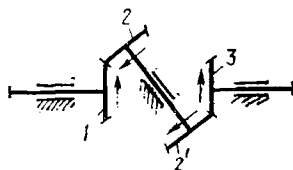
Двухступенчатый зубчатый механизм с коническими колесами
